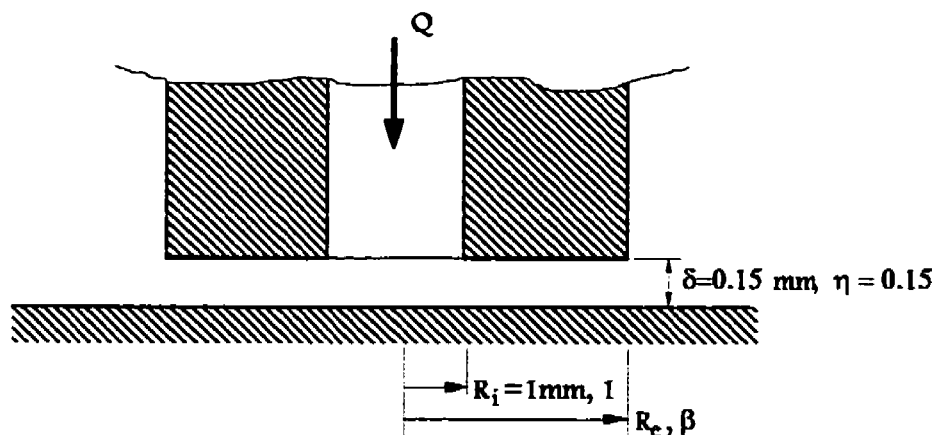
SURFACE FRONTALE DE LA BUSE DE SOUFFLAGE
